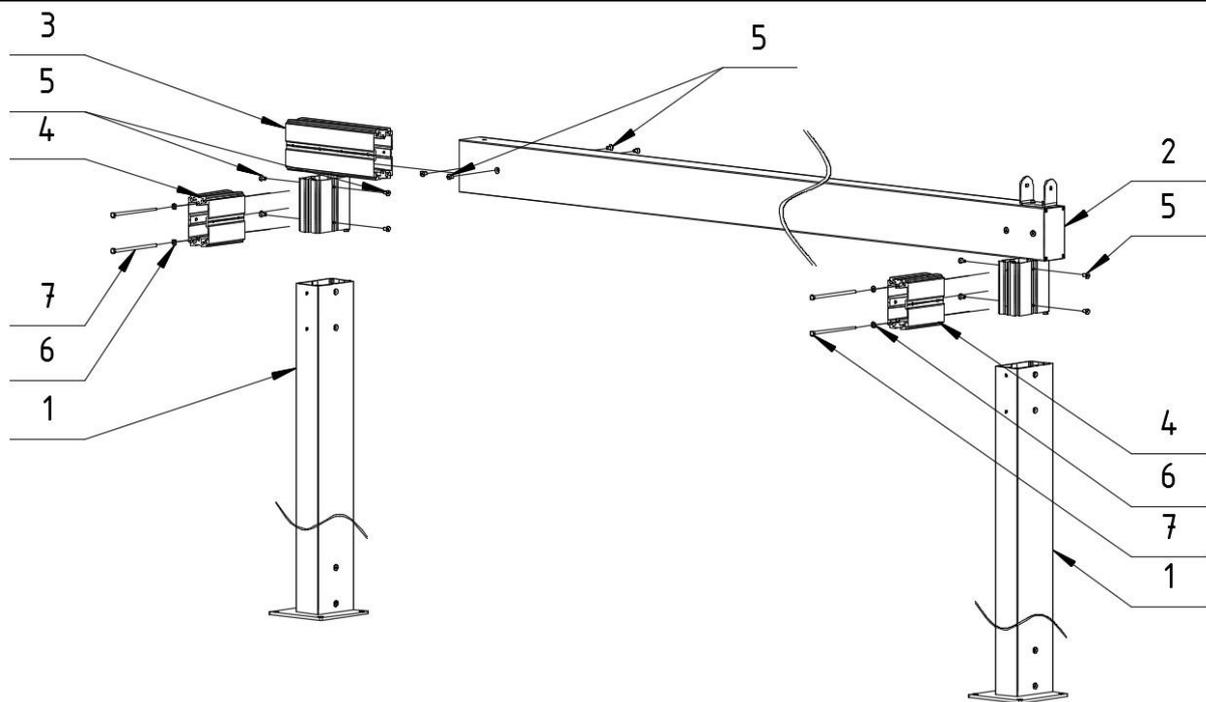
Méthode d'installation de la poutre avant du premier module. 1 - Poteau bas, 2 - Poutre avant (gauche/droite), 3 Connecteur "Connexion module", 4 - Connecteur linéaire, 5 Vis M8x16, 6 - Rondelle ø8.4, 7 - Vis M8x180.
